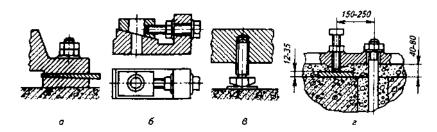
Приспособления для выверки расположения машины по высоте
